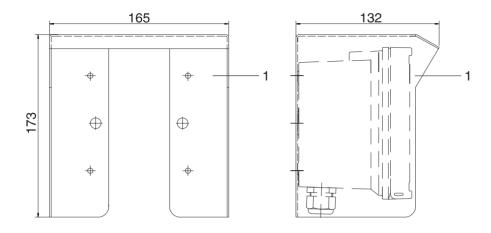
Tampa protetora ZU 0276 para montagem em parede e tubulação
